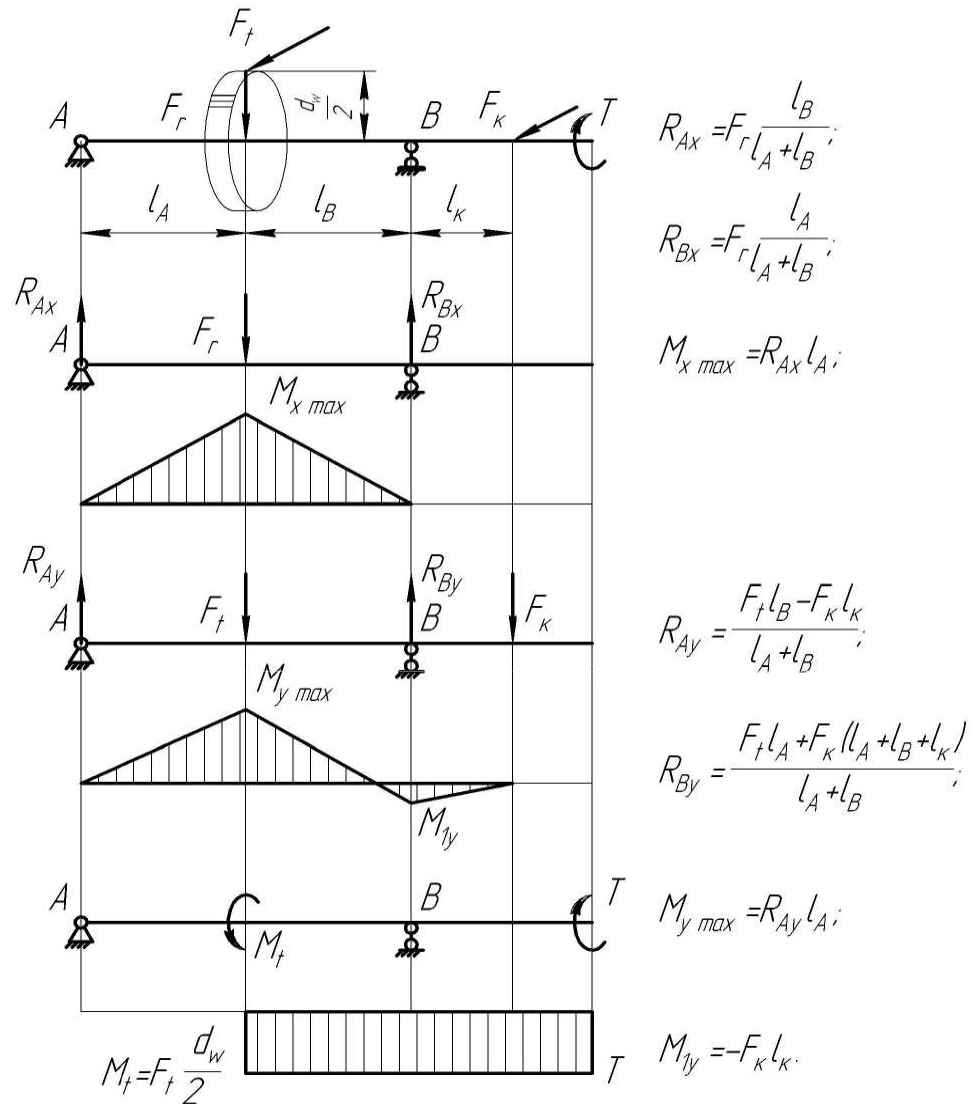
Розрахункова схема ведучого / веденого вала циліндричної прямозубої передачі.
